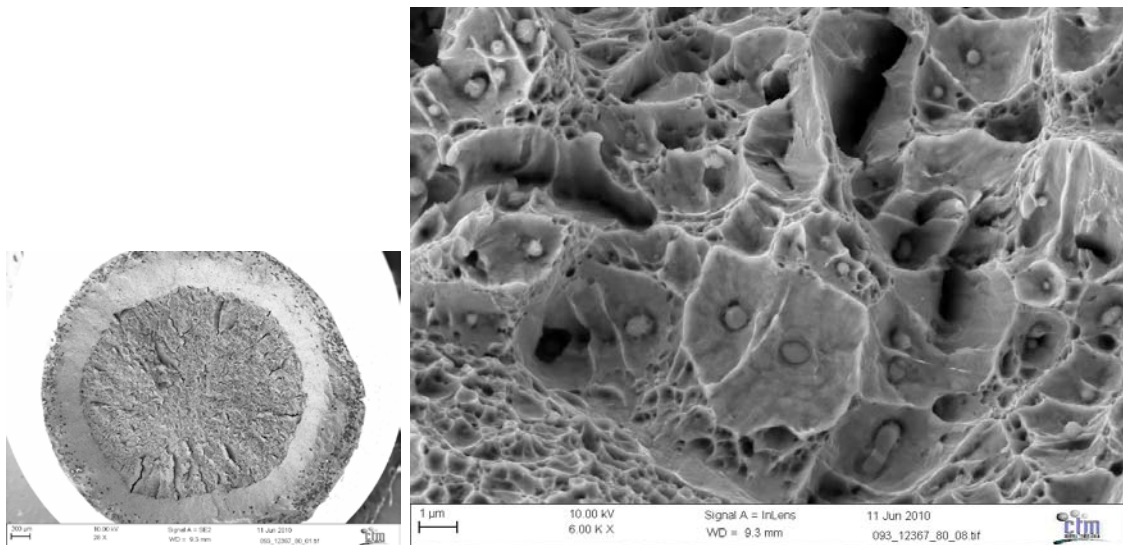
Superfície de fractura, sense zona d'inici, típica fractura dúctil.
